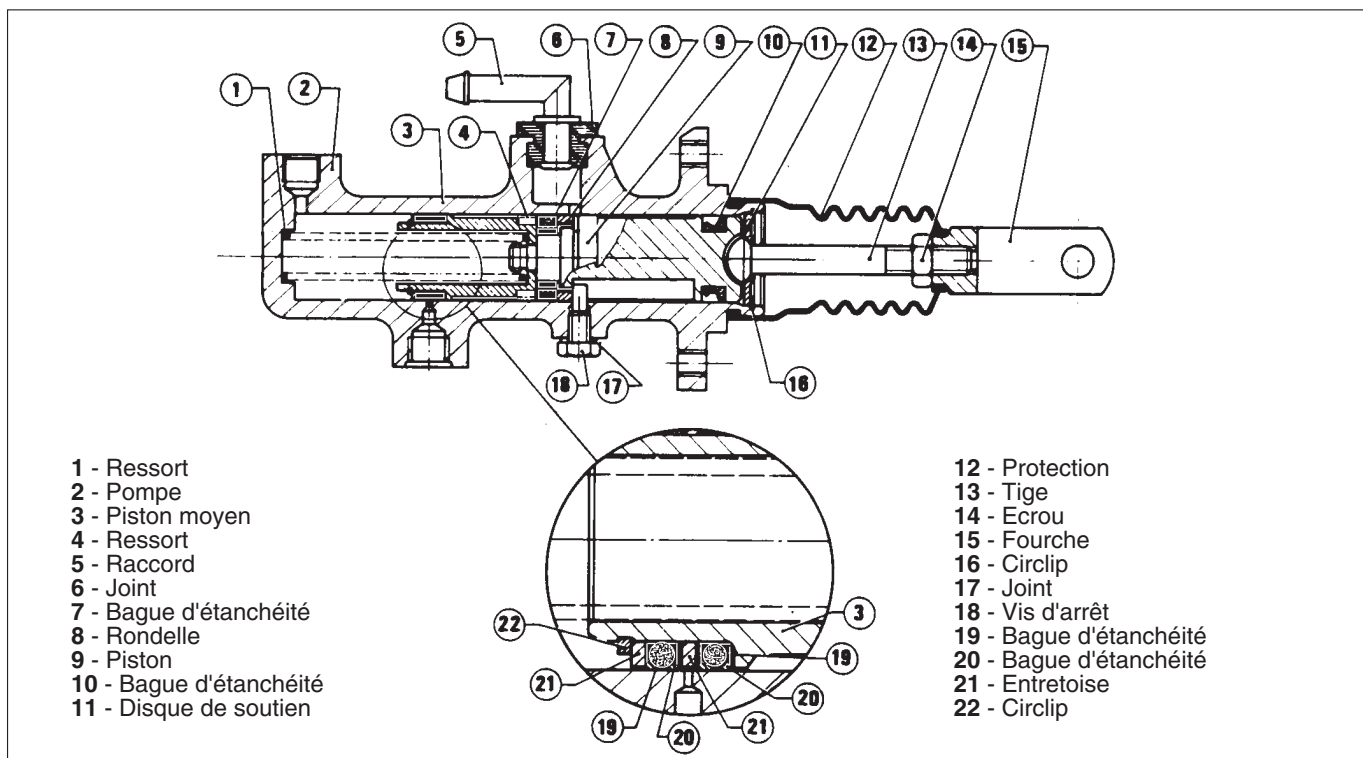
Vue en coupe de l'ensemble de pompe de freins.
